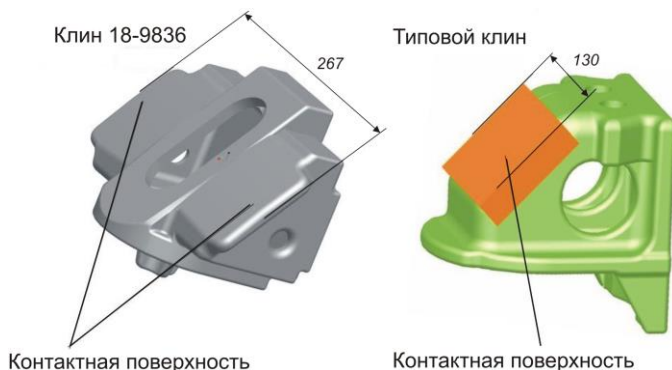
Отличия в конструкции клиньев тележки модели 18-9836 и типового
